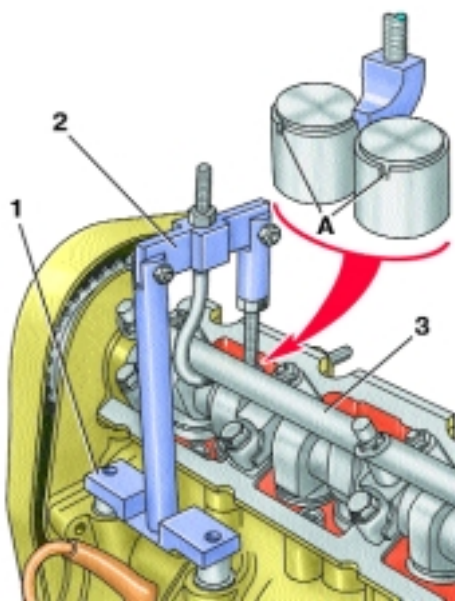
Установка приспособления для отжатия и фиксации толкателей клапанов двигателя мод. F3R 272: 1 – опора; 2 – приспособление для отжатия толкателей; 3 – рейка
